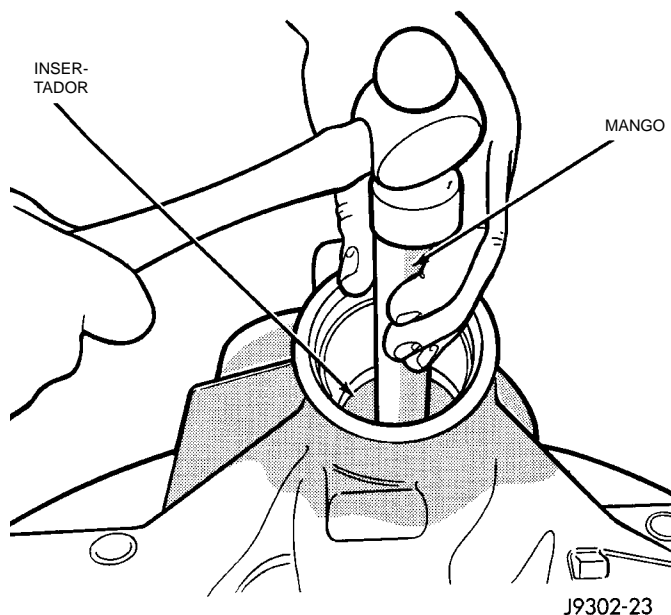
Desmontaje de la cubeta del cojinete trasero
